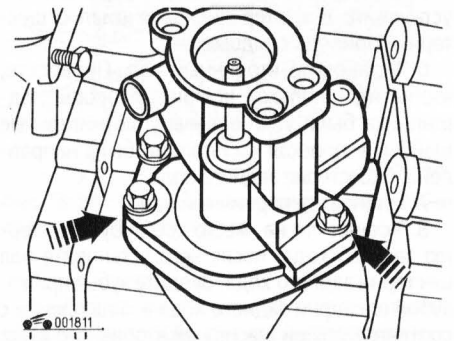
Расположение болтов крепления вала механизма переключения передач
